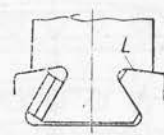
Coadă de rândunică cu fixare laterală prin pene.
